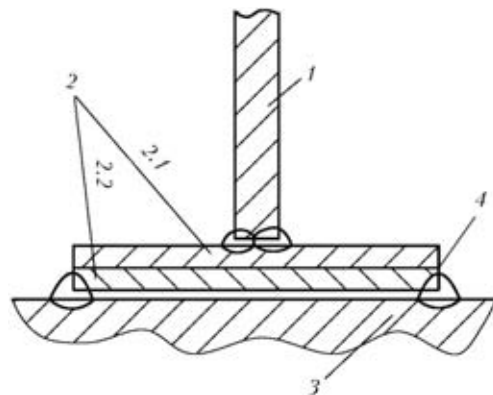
Схема выполнения соединения алюминиевой конструкции со стальной, полученного с использованием переходного биметаллического элемента: 1 — алюминиевый сплав марки 1561; 2 — биметалл (2.1 — алюминиевый сплав марки 1560; 2.2 — аустенитная хромоникелевая сталь марки 10X18H10T); 3 — судокорпусная низколегированная сталь типа Д40; 4 — возможный очаг расслоения
